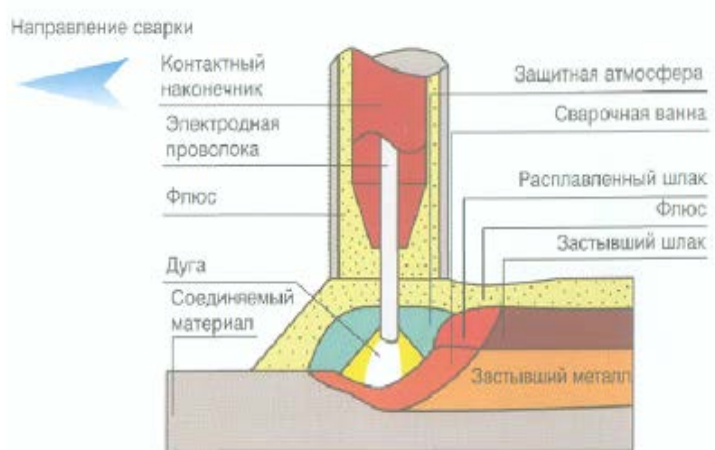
Автоматическая сварка под слоем флюса
